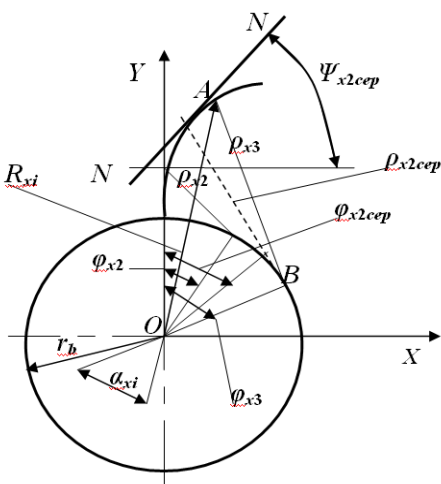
Схема для профілювання дійсного робочого профілю зубця колеса
